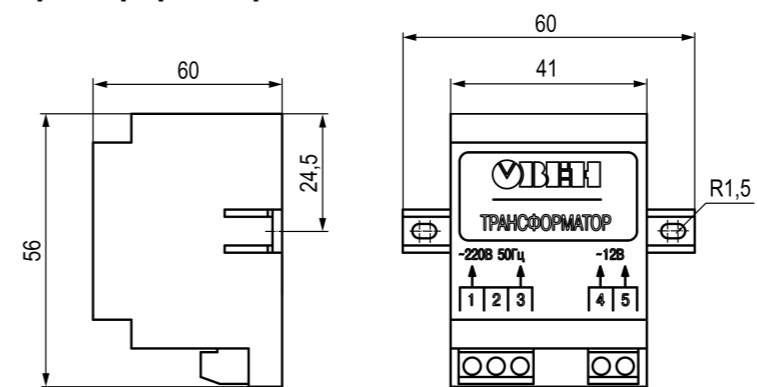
Габаритные и установочные размеры трансформатора ТПК-121-К40
